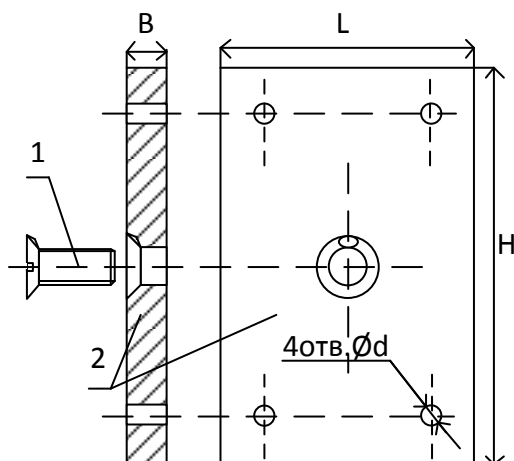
(1- болт для крепления изолятора к площадке, 2-площадка для монтажа к стене)
